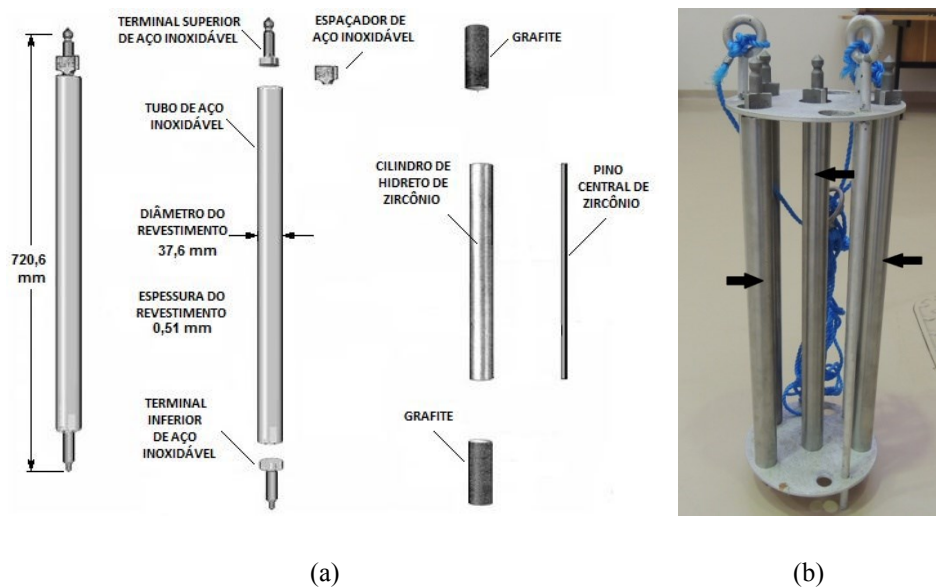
Elemento combustível do reator TRIGA IPR-R1. Geometria e componentes do elemento (a); elemento combustível instrumentado montado (b).
